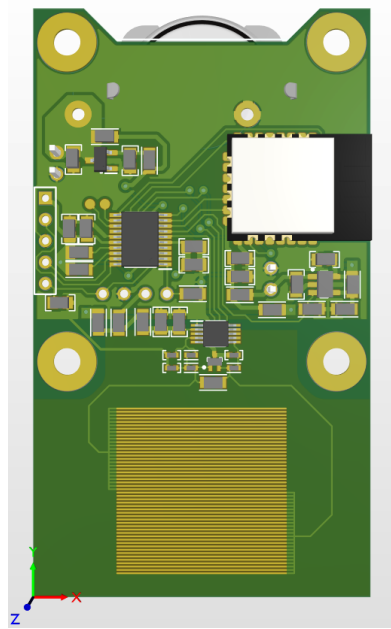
’de PCB tasarımının Bottom Layer olarak adlandırılan alt yüzeyi gösterilmiştir. Tasarımdan anlaşılabileceği üzere 2 Layer 1,6 mm FR4 dolgu malzemeler PCB ile tasarım yapılmıştır.
